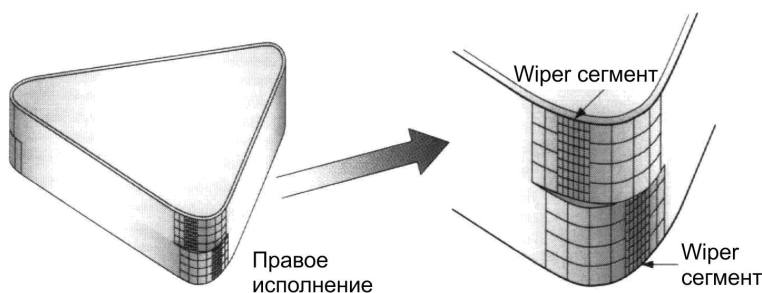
Режущая пластина Secomax CBN100 Crossbill
